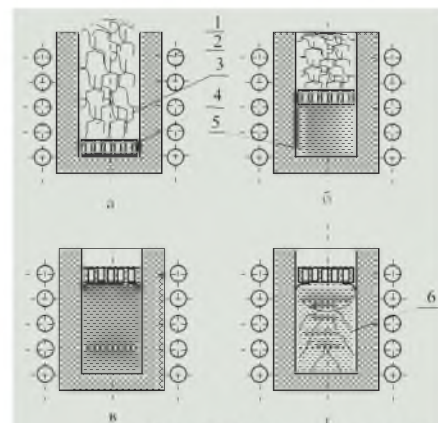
Схема способа рафинирования расплава отходов меди: а – загрузка шихты; б – процесс плавления шихты; в – полное расплавление; г – направленное затвердевание; 1 – индуктор; 2 – тигель; 3 – шихта; 4 – графитовая шайба; 5 – медный расплав; 6 – затвердевающая литая заготовка
